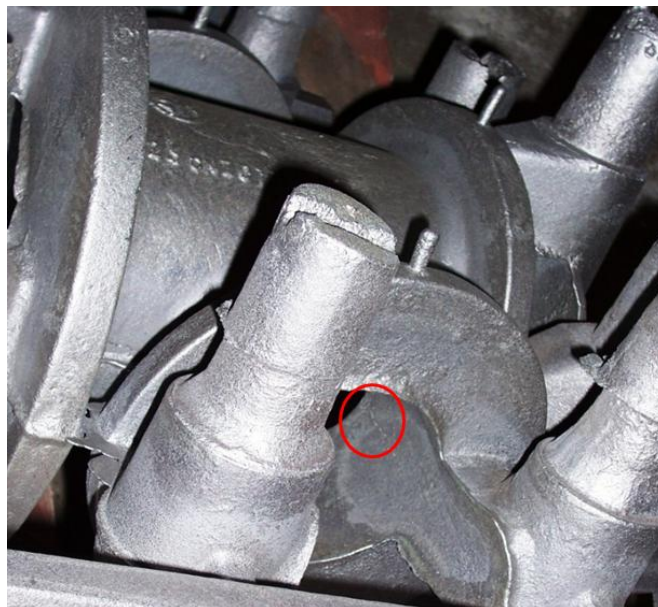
Pormenor de uma fissura na zona interior da peça.
